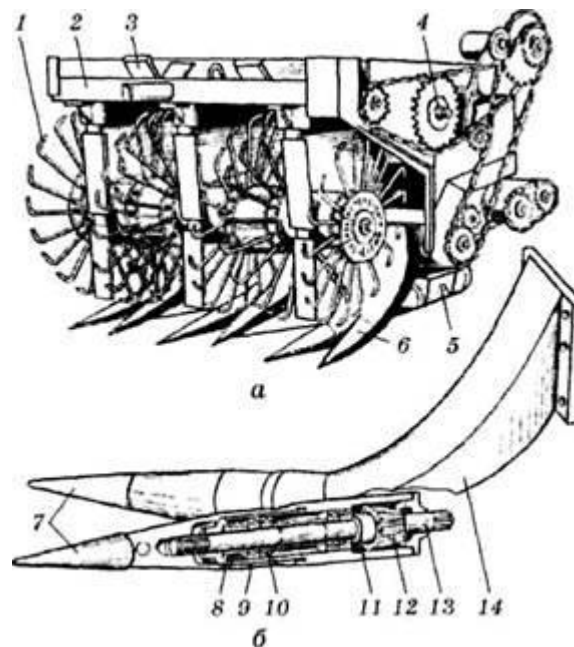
Викопувальний пристрій коренезбиральної машини МКК-6-02:
